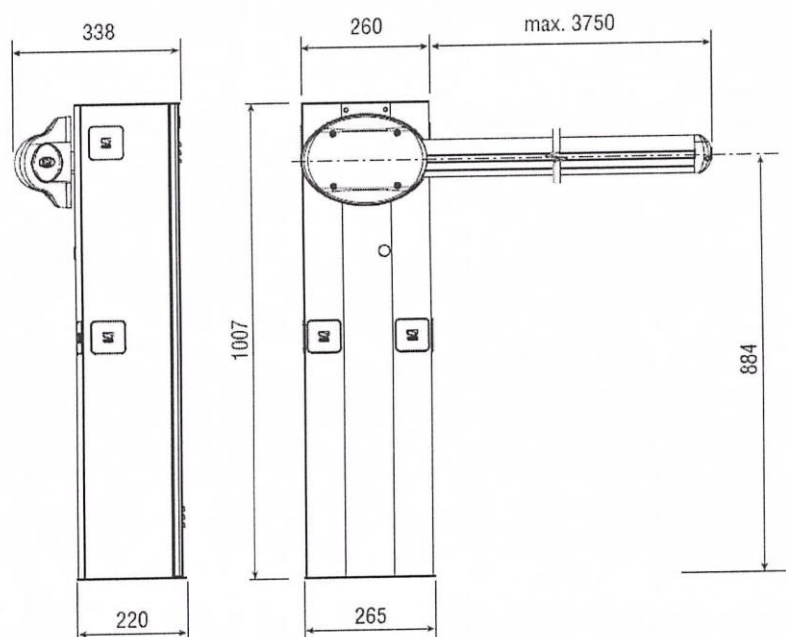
Габаритные размеры шлагбаума CAME GARD 3750
